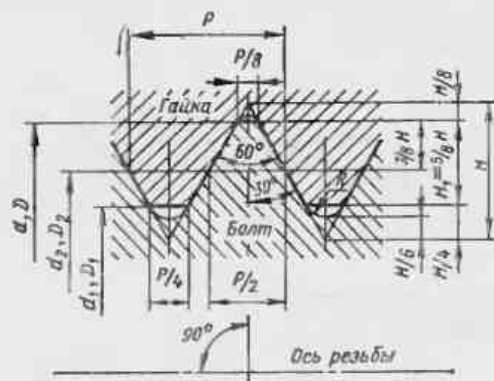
Профиль и основные параметры метрической резьбы для диаметров от 1 до 600 мм
